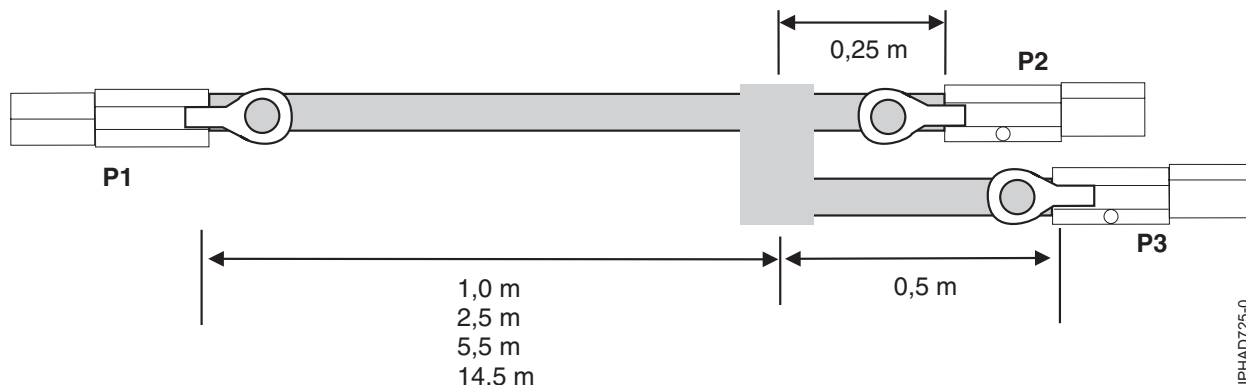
Longituds de cables de conjunt de cable YO SAS extern
